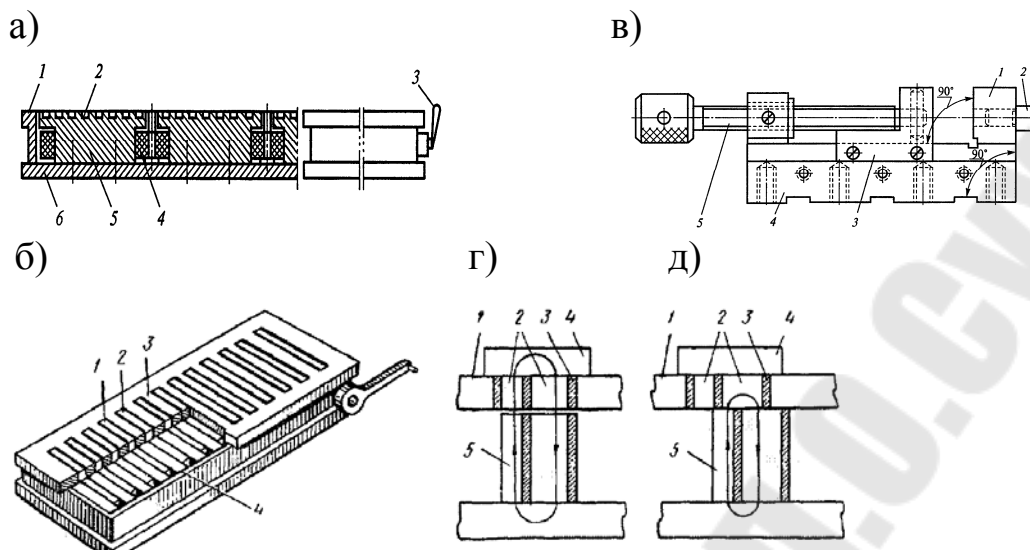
Устройства для закрепления шлифуемых заготовок:
